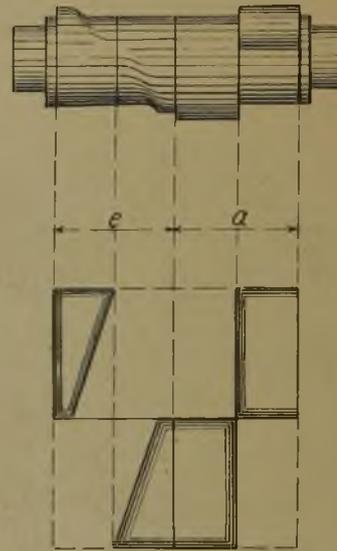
Steuerknaggen einer Fördermaschine. in der Weise ergänzt, daß außer den 4 Knaggen für die beiden Einlaß- und Auslaßventile (e bzw. a in Fig. 43) 4 weitere für das Ansaugen (s) und Heraus-
